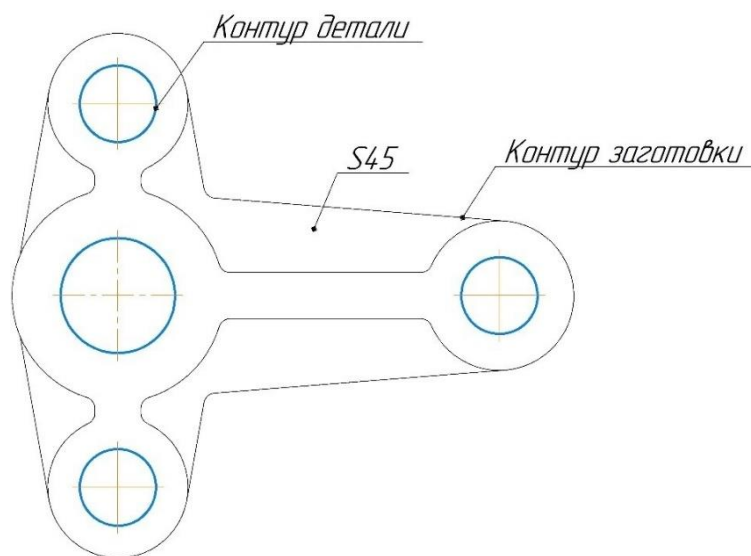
Эскиз заготовки для изготовления детали рычаг
